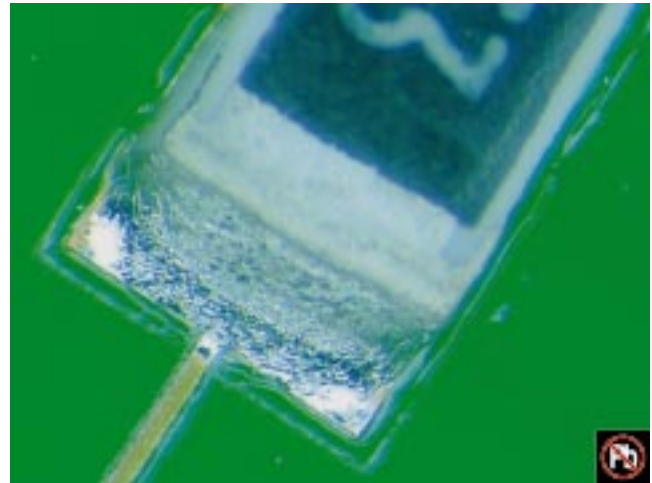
Soldadura SnAgCu; Proceso No-Lavable
